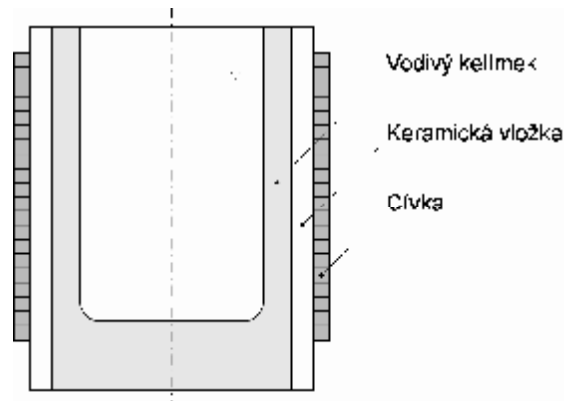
Indukční kelímková pec se železným jádrem vně cívky
